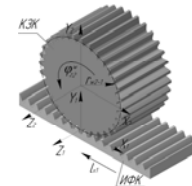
Кинематическая схема формообразования, т.е. относительного движения исходного формообразующего реечного контура в системе координат заготовки контура зубчатого колеса (для наглядности изображена объемная модель пары рейка-колесо)
